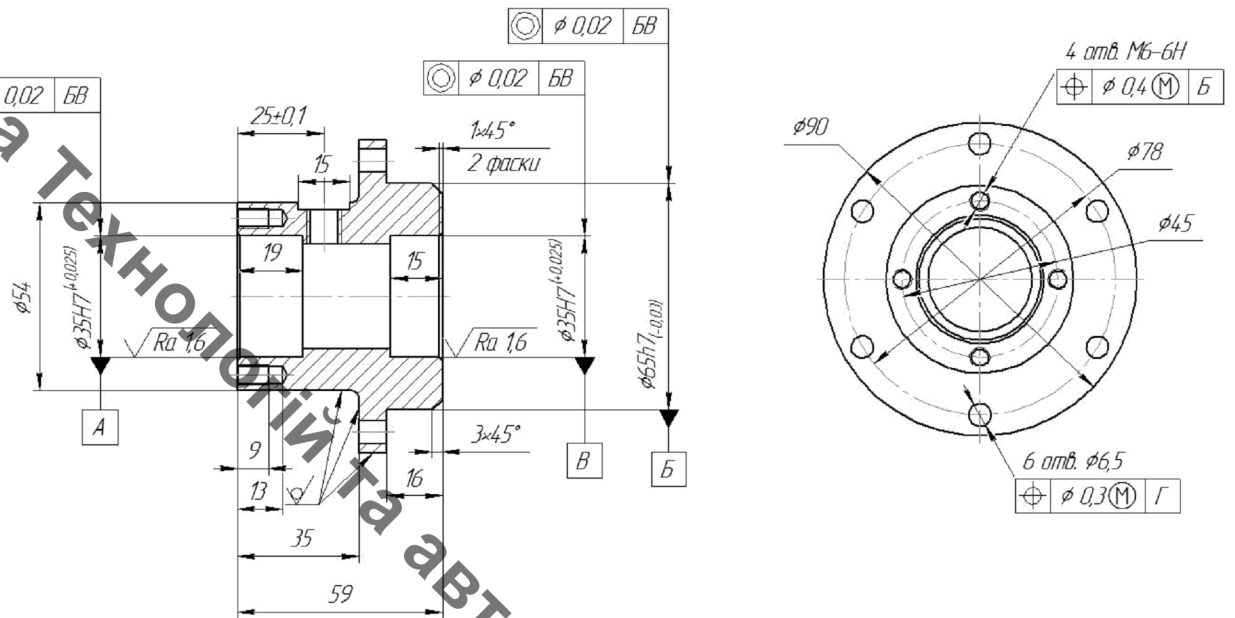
Характерні поверхні деталі Корпус 46-76
